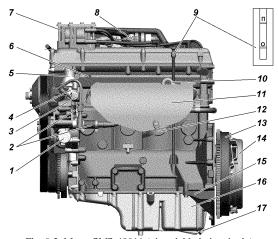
Motor 3M3-40911 (vista del lado izquierdo):
